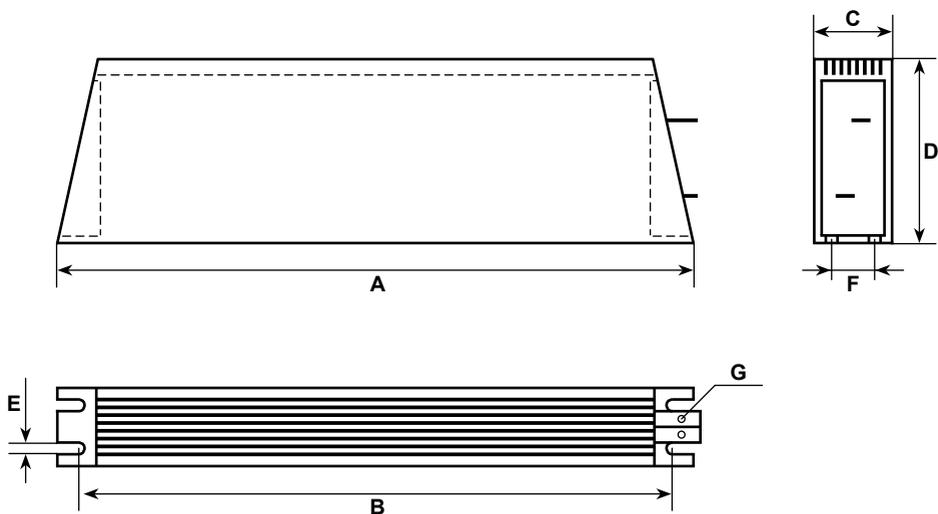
Внешний вид тормозного резистора LCR на 1-6 кВт
